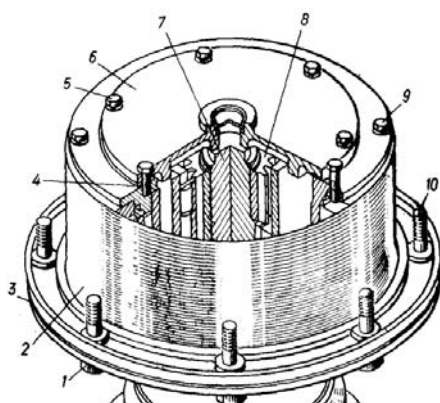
Снятие водила, полуосей: 1 — гайка; 2 — водило; 3, 4 — прокладка; 5, 10 — болт; 6 — крышка; 7 — полуось; 8 — колесо зубчатое; 9 — пробка
